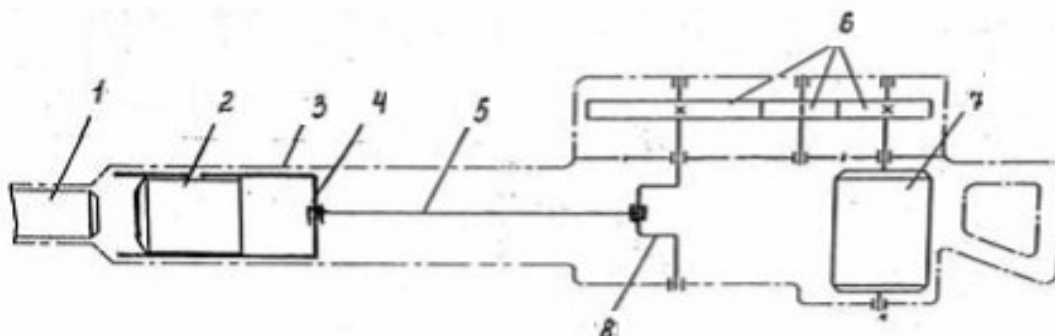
Принципиальная схема привода ручных ударных машин с кривошипно-шатунным преобразовательным и компрессионно-вакуумным ударным механизмом с подвижным направляющим цилиндром (электроломоток): 1 - хвостовик инструмента; 2 - ударник; 3 - корпус машины; 4 - подвижный направляющий цилиндр с окнами; 5 - шатун; 6 - редуктор; 7 - двигатель; 8 – кривошип.
